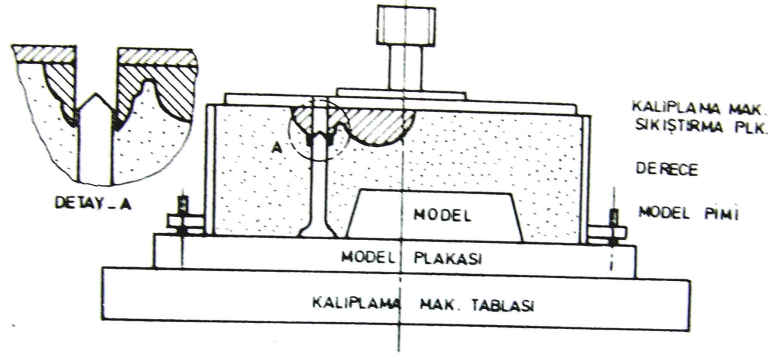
Özel şekilli döküm hunisi ve boyutları
